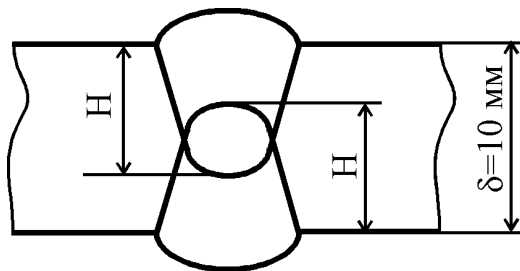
Стыковое соединение с двусторонним проплавлением
